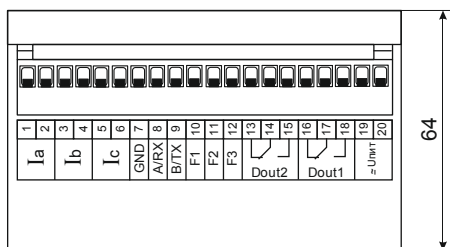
Габаритные и установочные размеры ЭКТМД2 без датчиков тока для крепления на DIN-рейку 35 мм.
